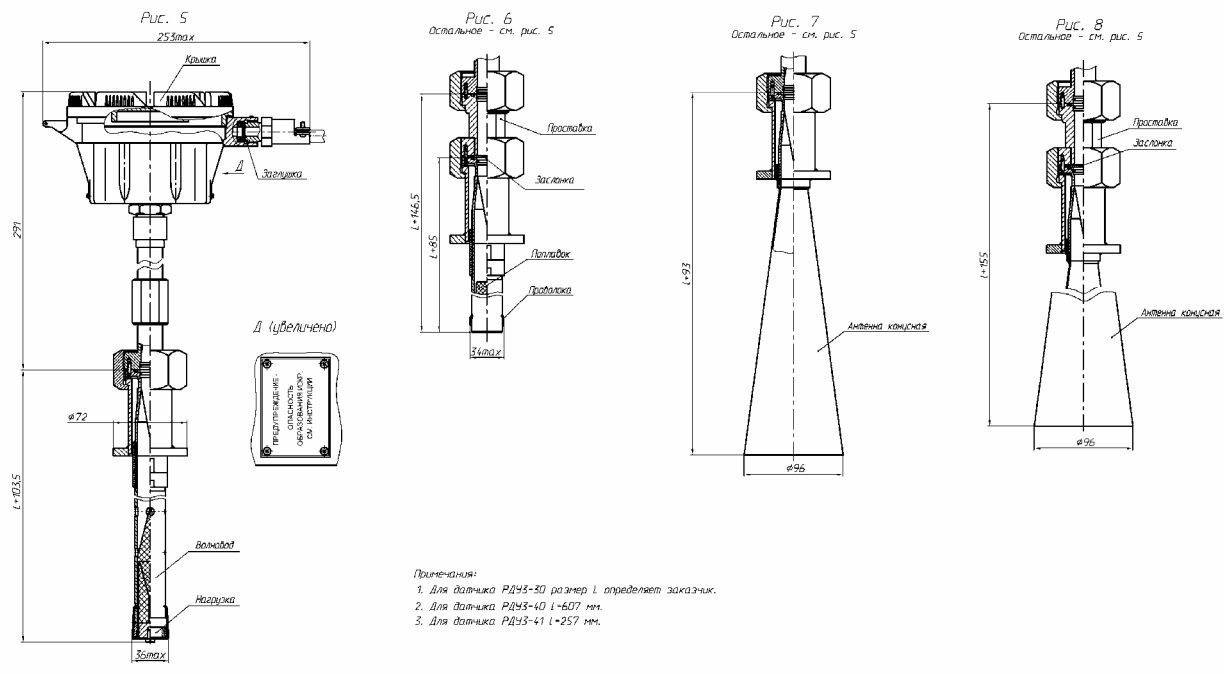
Габаритные и установочные размеры датчиков РДУЗ-30, РДУЗ-40, РДУЗ-41, часть 2
